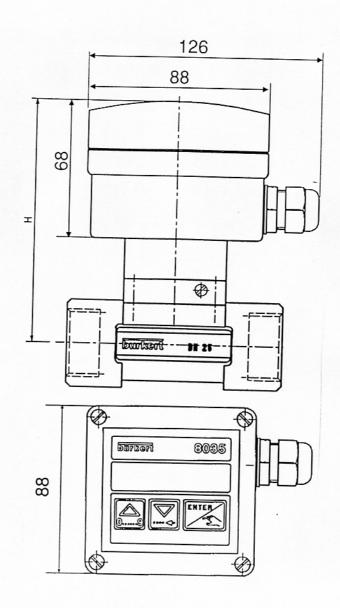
Dimensioni esterne del corpo elettronico SE35.
